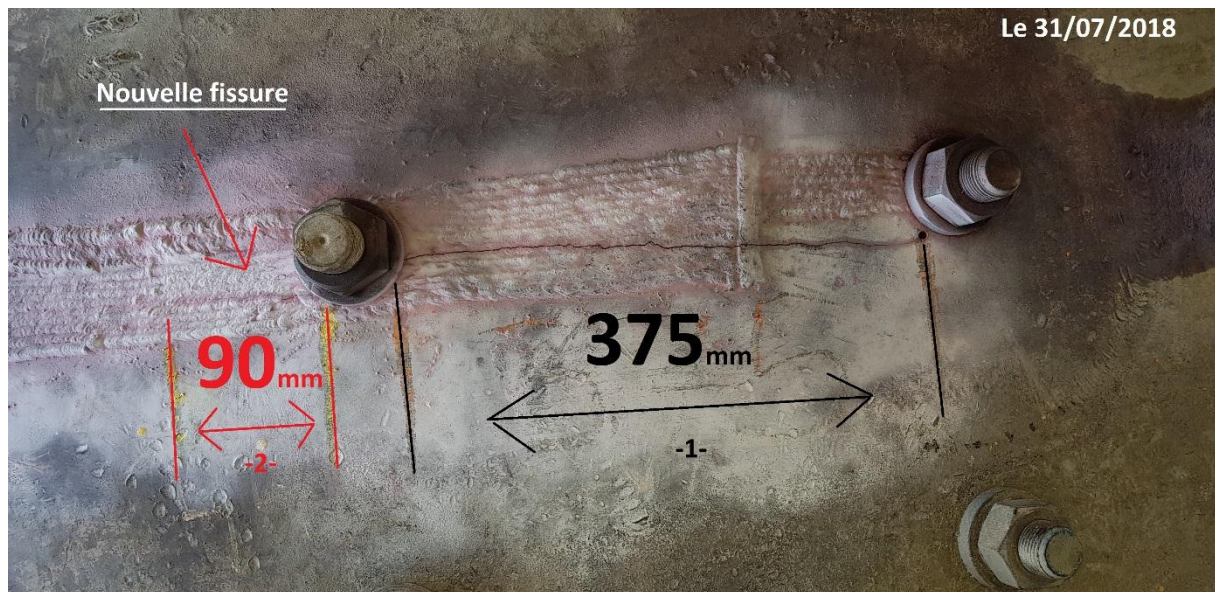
fissure apparue sur la virole d'une longueur de (375mm et 90mm).
